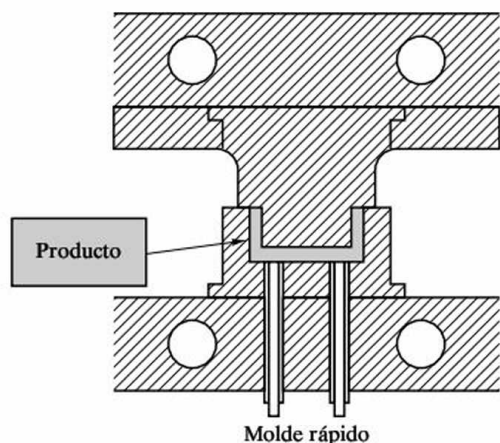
Esquema de una máquina de moldeo por compresión de termoestables.
